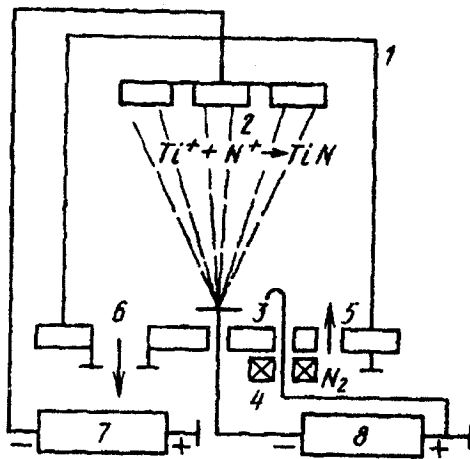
Принципова схема вакуумно-плазмової установки для реалізації методу КІБ: 1 – корпус вакуумної камери; 2 – різальні інструменти; 3 – випарювальний прилад; 4 – електромагніти; 5 – прилад подачі реакційного газу; 6 – вакуумний насос, 7, 8 – джерела живлення
